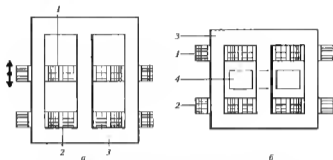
Схемки трансформатор сварочного выпрямителя с подвижными катушками (*а*) и подвижным магнитным шунтом (*б*)
